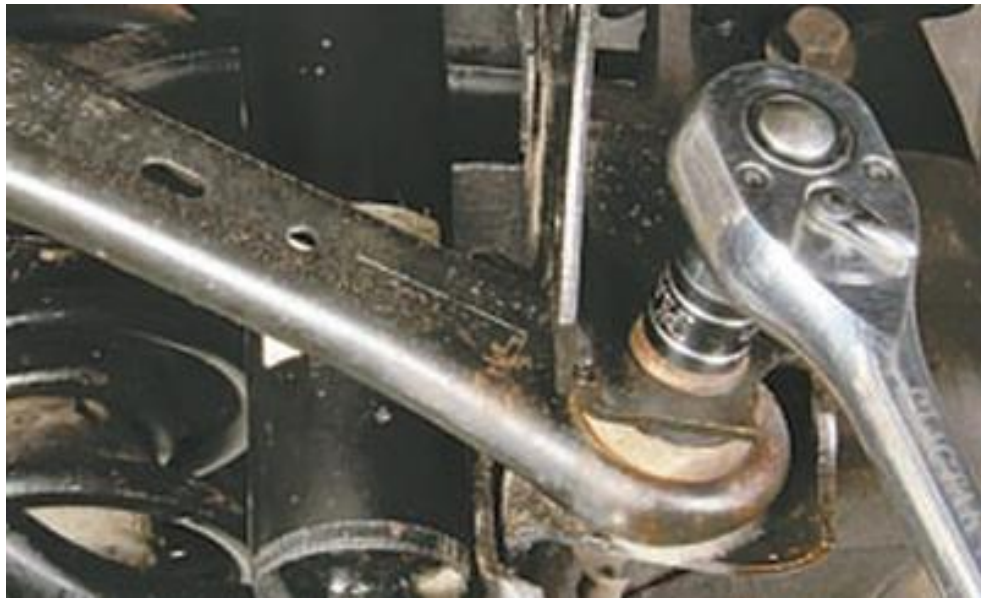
Відкручування болта кріплення поперечного важеля
